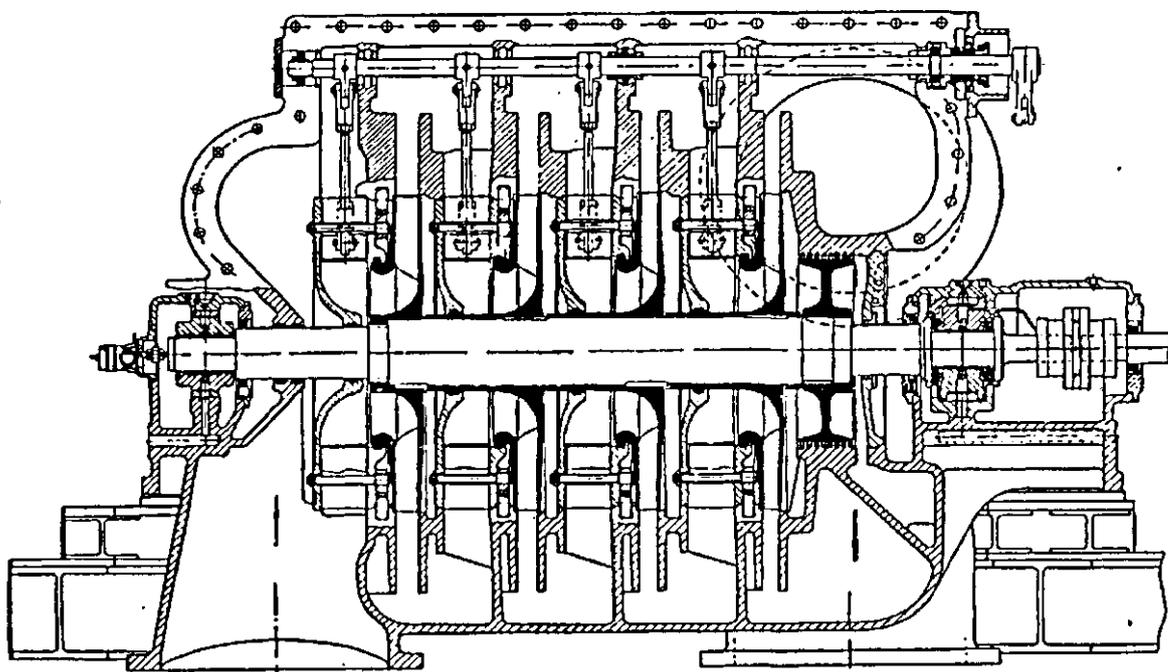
Четырехступенчатая воздуходувка фирмы «Алис-Чалмерс» с направляющими лопатками на каждой ступени
